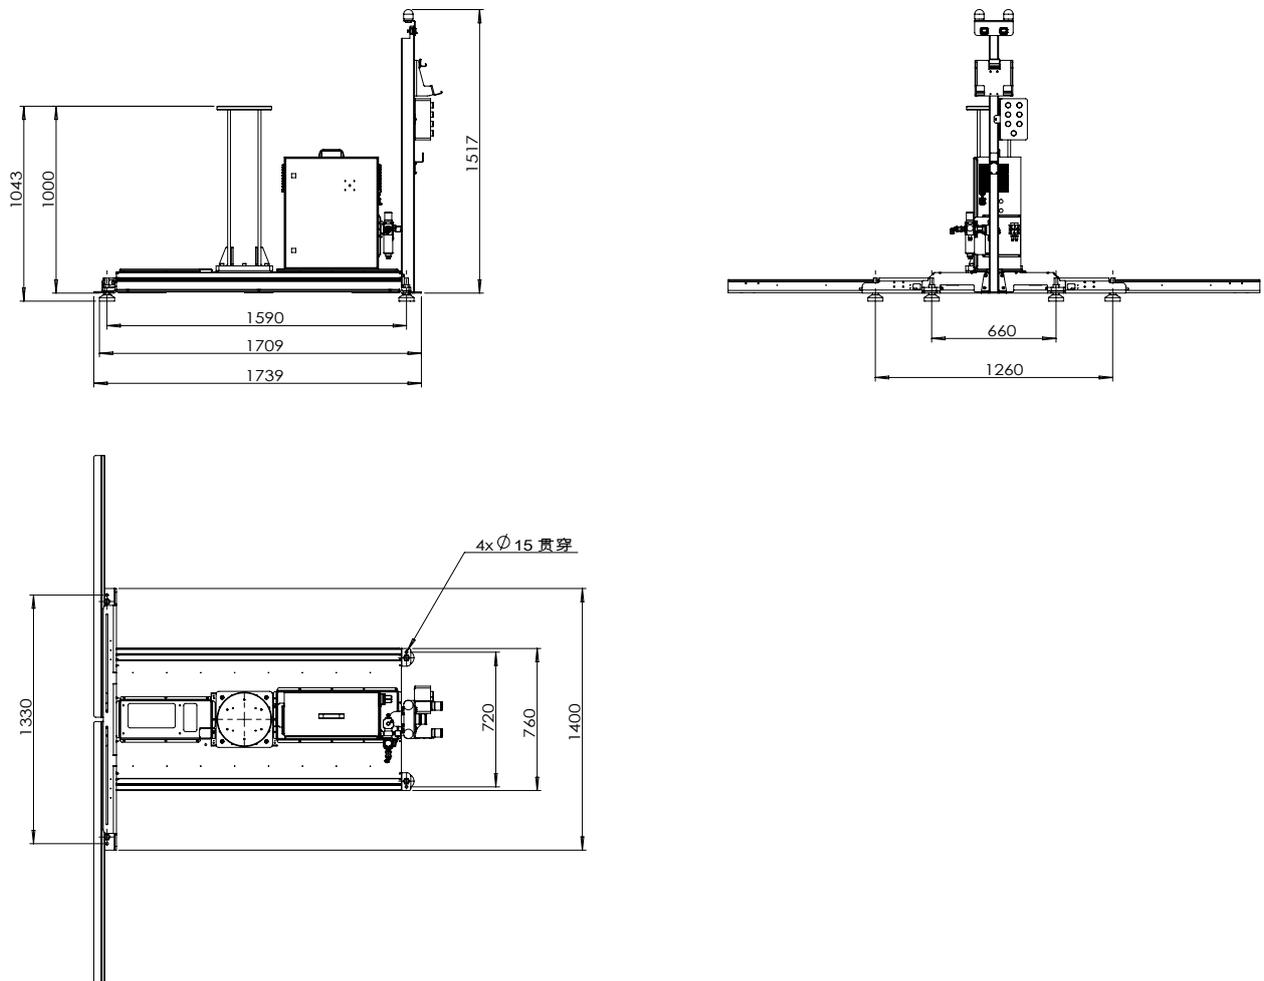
CPF10 尺寸图, 图示尺寸单位为 mm
